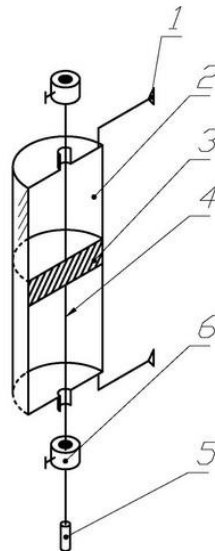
Молотковий механізм з приводом від пневматичного циліндру
